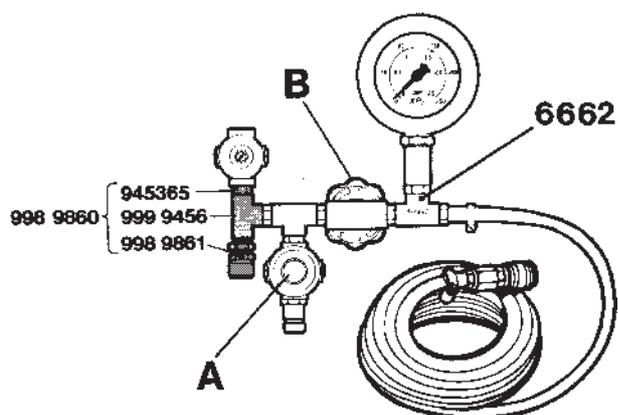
Montage du kit 998 9860 sur le dispositif d'essai sous pression 6662 (Suède seulement)
